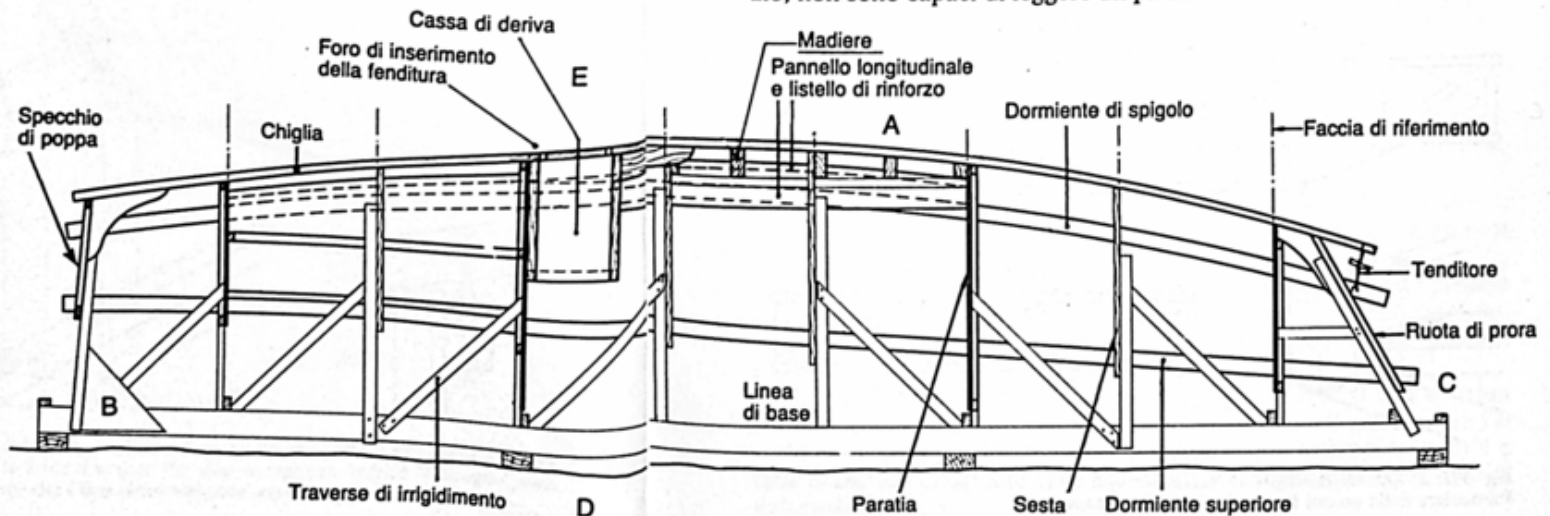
Sezione longitudinale di uno stampo a perdere. Gli elementi strutturali sono segnati con linee marcate; quelli provvisori, con linee sottili.
